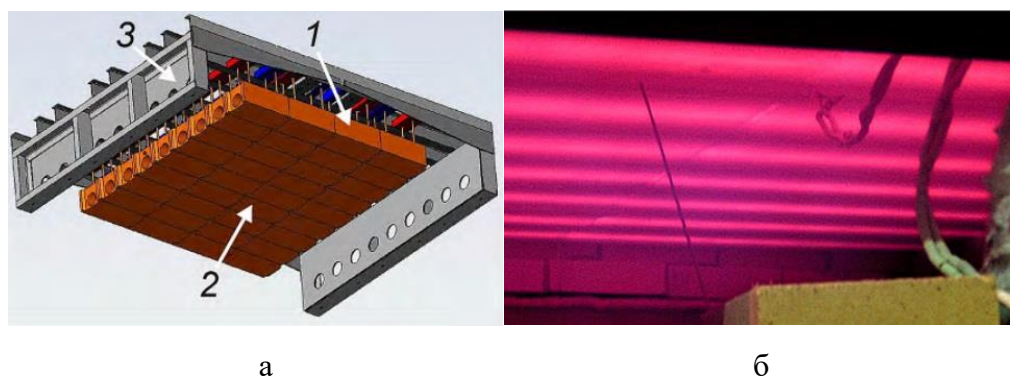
Вид нагревателя «Светящийся свод»
